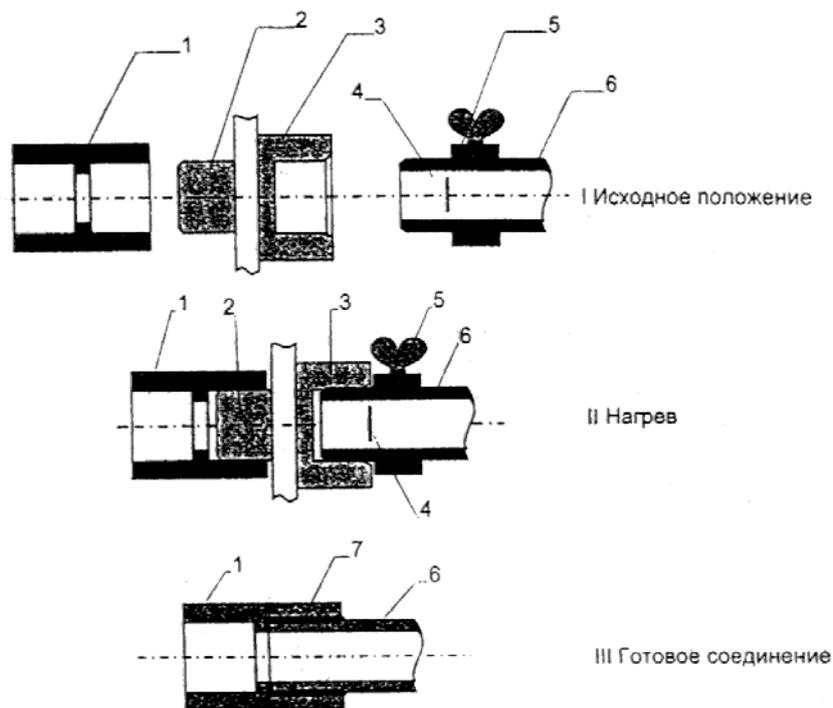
Последовательность процесса контактной сварки в раструб трубы и муфты из PPRC.
